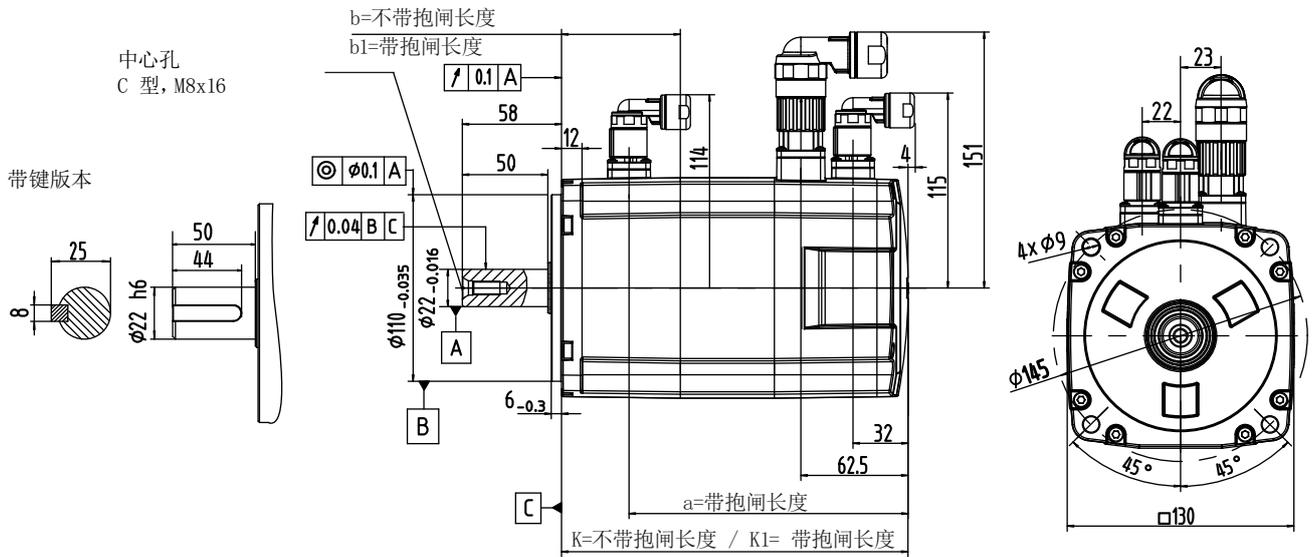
电机安装尺寸 (mm) - 轴高: 65 mm, 带增量式编码器
